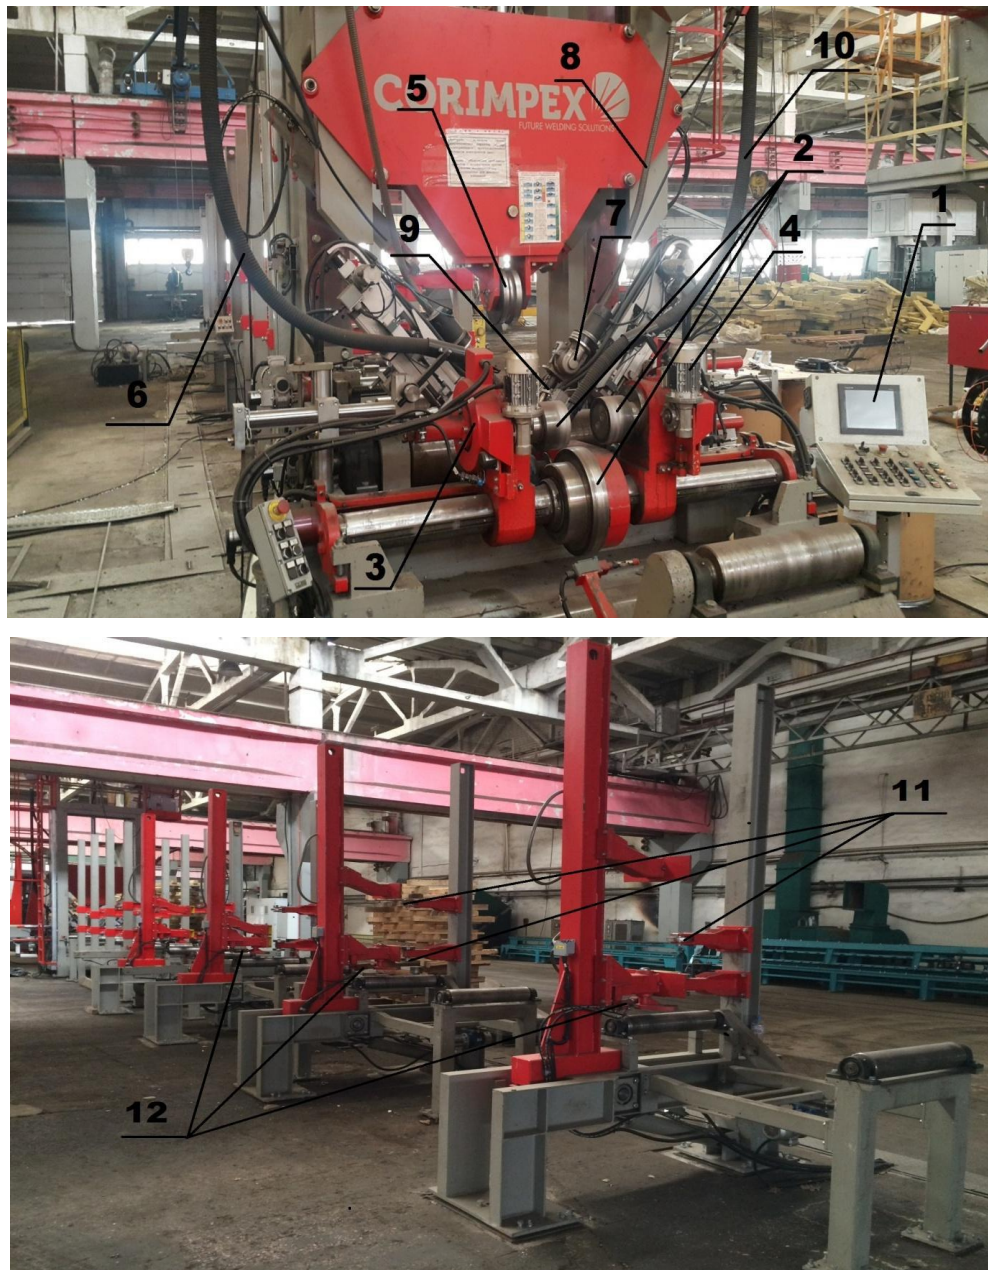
Зварювальна ділянка установки Corimpex BWM 1200x600:
